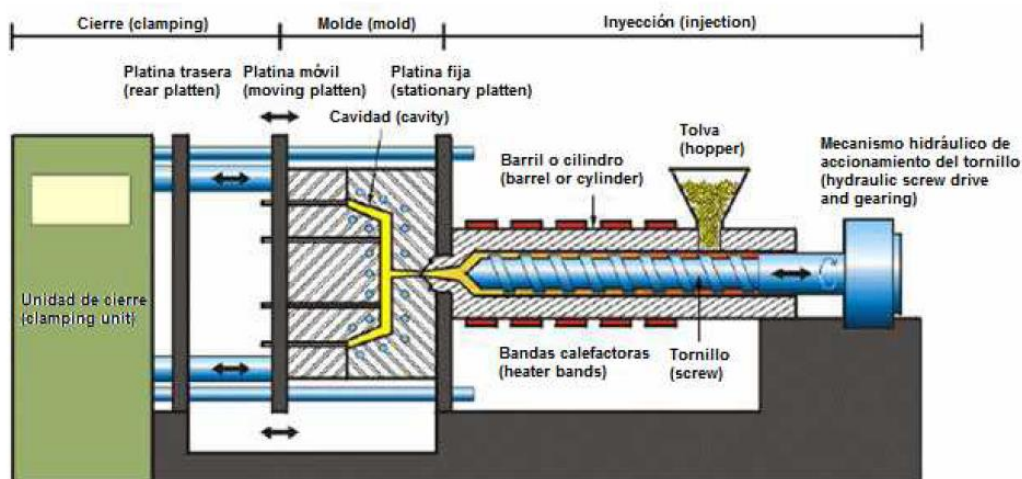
Maquinaria utilizada en proceso de inyección por molde
